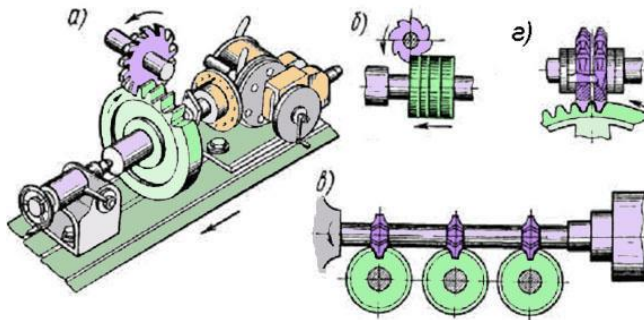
Нарізання зубів дисковими модульними фрезами
